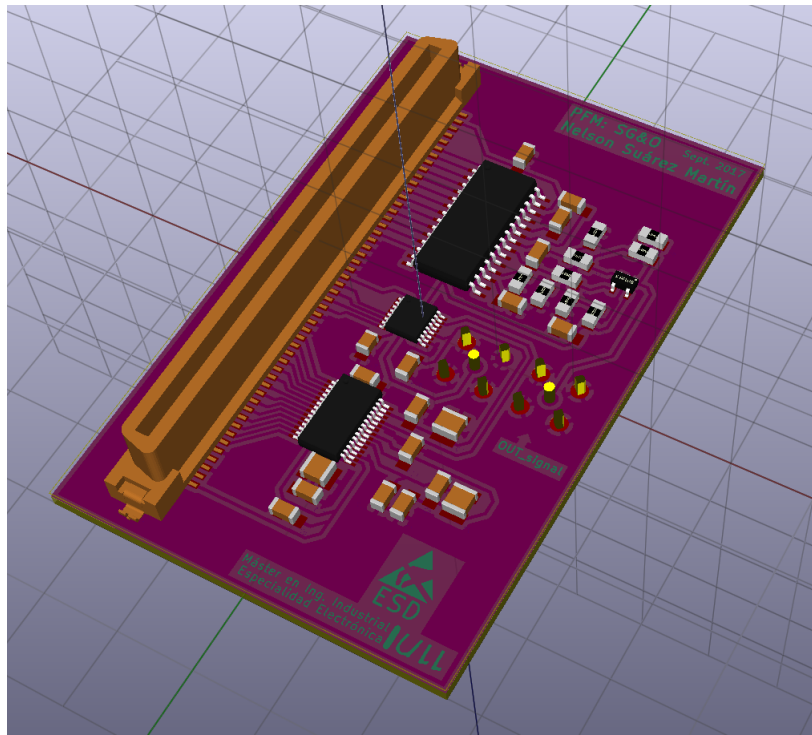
Vista frontal de la PCB fabricada. *Modelo 3D extraído de KiCad*.
